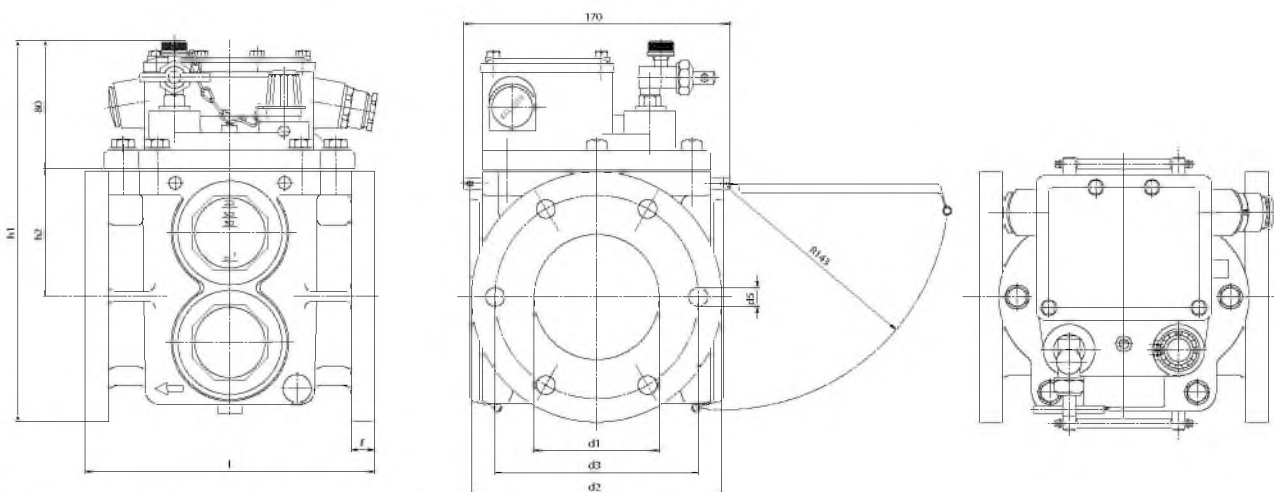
Размерный эскиз типов 52, 53
